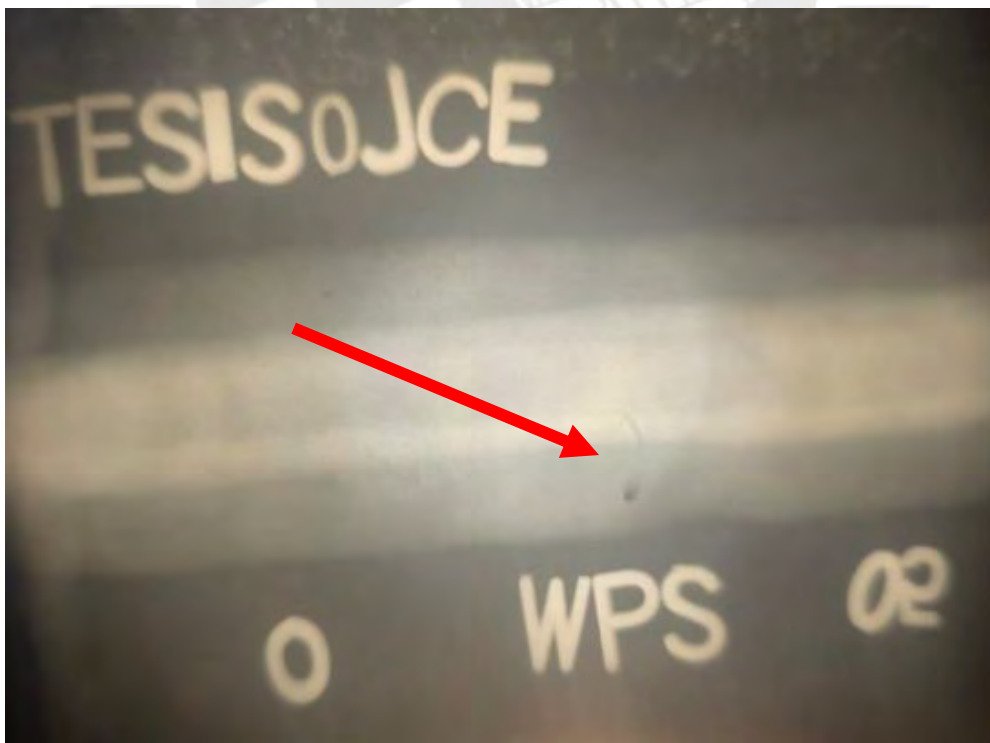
Porosidad vermicular en cupón WPS-02 soldado con FCAW
